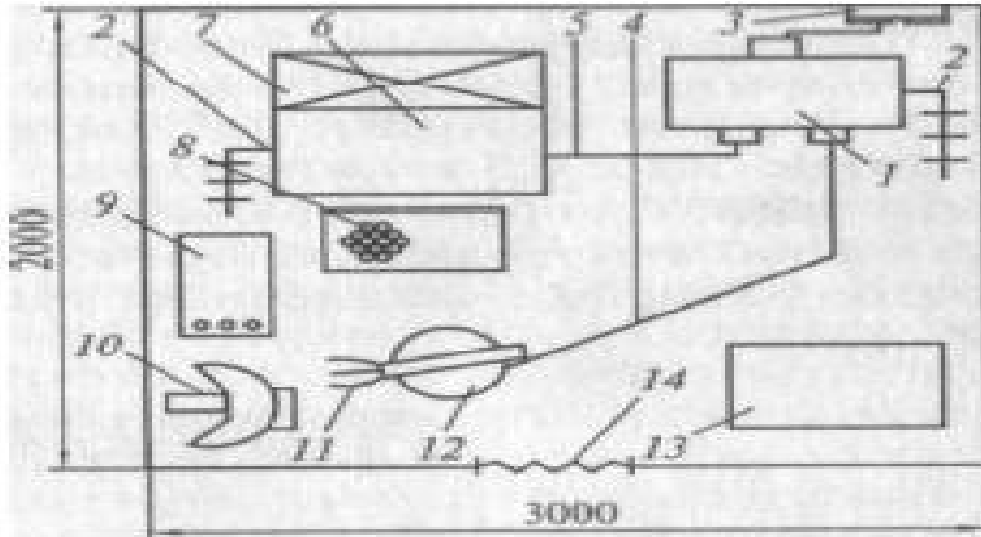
Планировка сварочной кабины:
